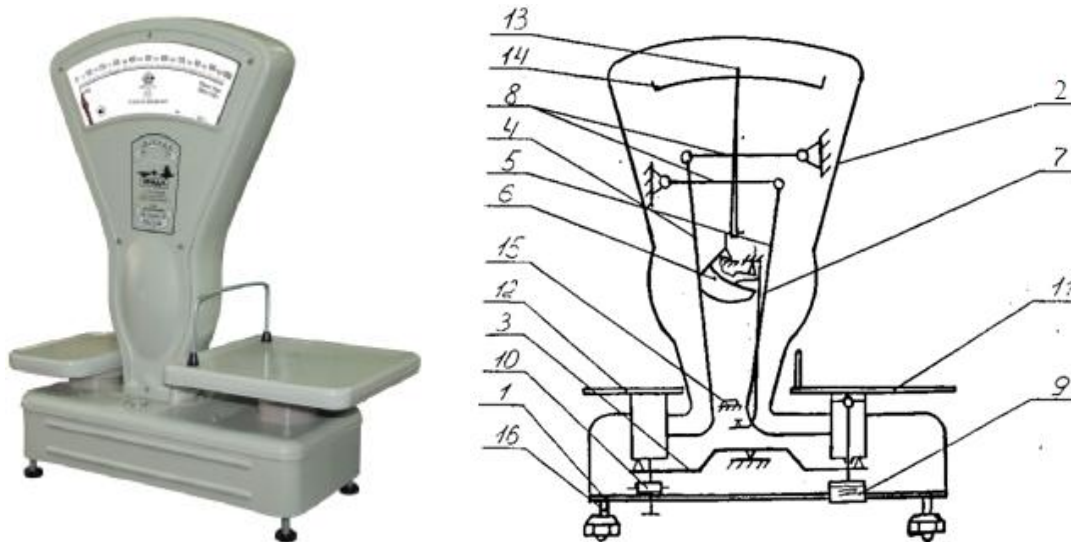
Общий вид и схематичное изображение весов (1 – плита; 2 – корпус; 3 – основной равноплечий рычаг; 4 – грузовой рычаг гиревой платформы; 5 – грузовой рычаг грузовой платформы; 6 – квадрант; 7 – тяга; 8 – струнки; 9 – успокаитель колебаний; 10 – устройство арретирования; 11 – грузоприёмная платформа; 12 – гиревая платформа; 13 – стрелка; 14 – шкала; 15 – устройство установки по уровню; 16 – ножка)
